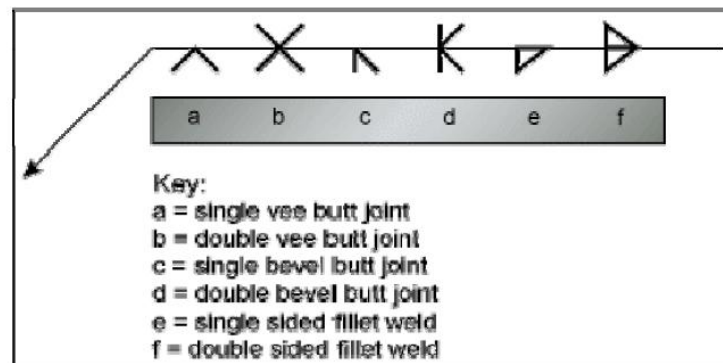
Símbolos de diferentes tipos de filetes de soldadura
